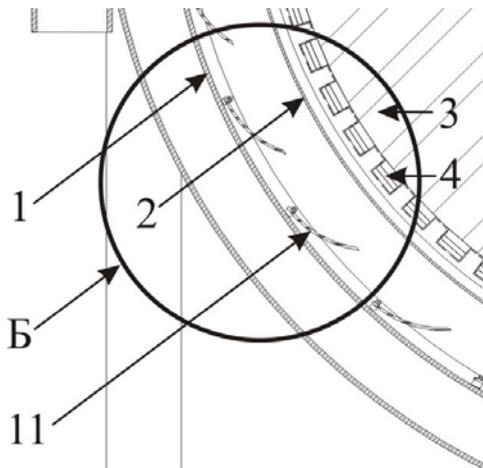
Увеличенный разрез условно принятой 2 четверти: 1 – корпус; 2 – немагнитный барабан; 3 – ярмо; 4 – магниты; 11 – лопастные дефлекторы
